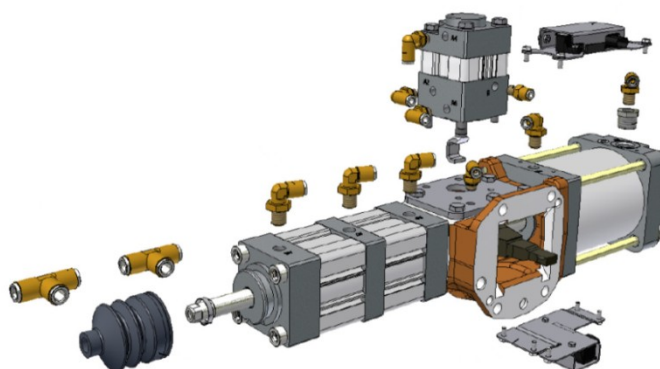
Řez pneumatickým posilovačem TATRA [4]
